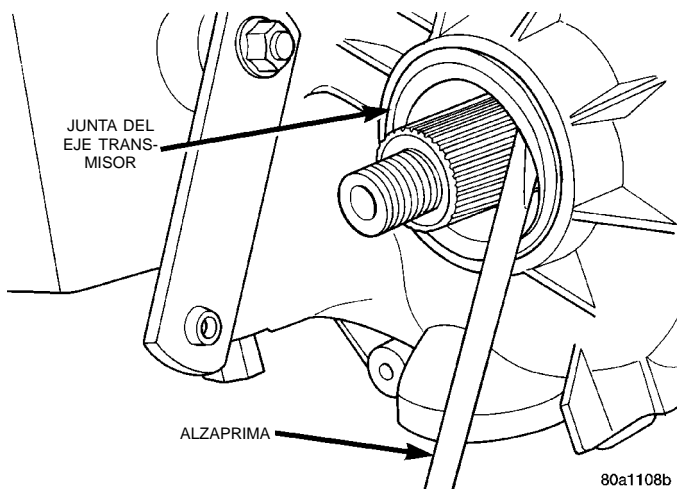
Desmontaje de la junta delantera del eje transmisor
